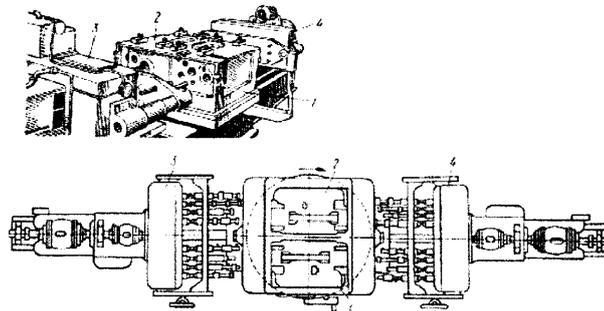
Агрегатный двусторонний станок мод. 2А774а с поворотным двухпозиционным столом для растачивания корпуса коробки скоростей токарного станка:
